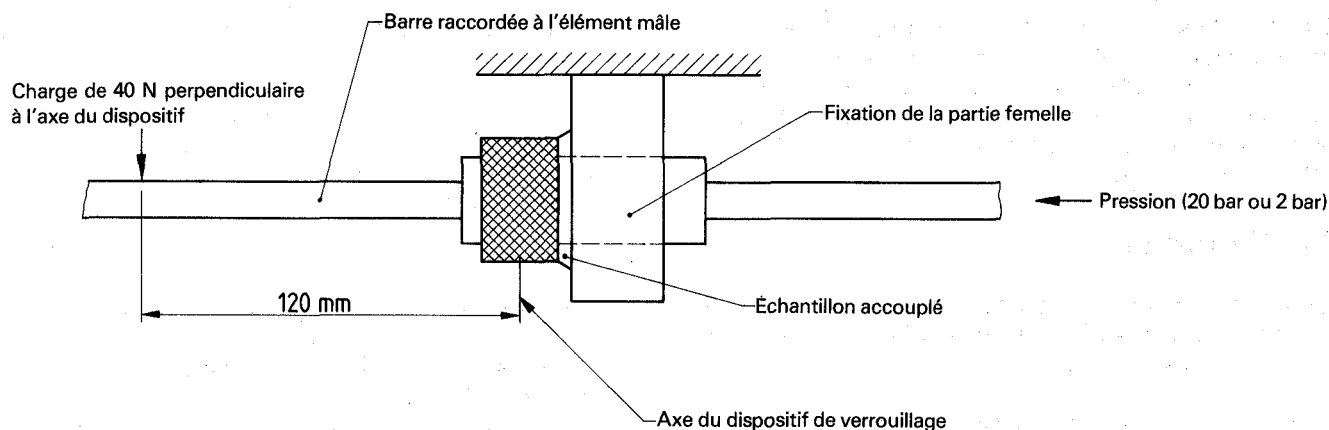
Montage pour l'essai d'étanchéité aux gaz en position accouplée
